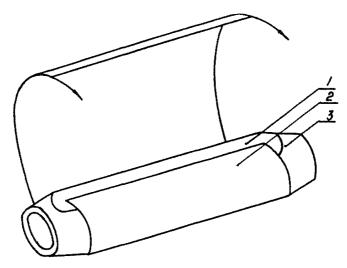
Намотка защитного слоя на корпус соединительного зажима:
